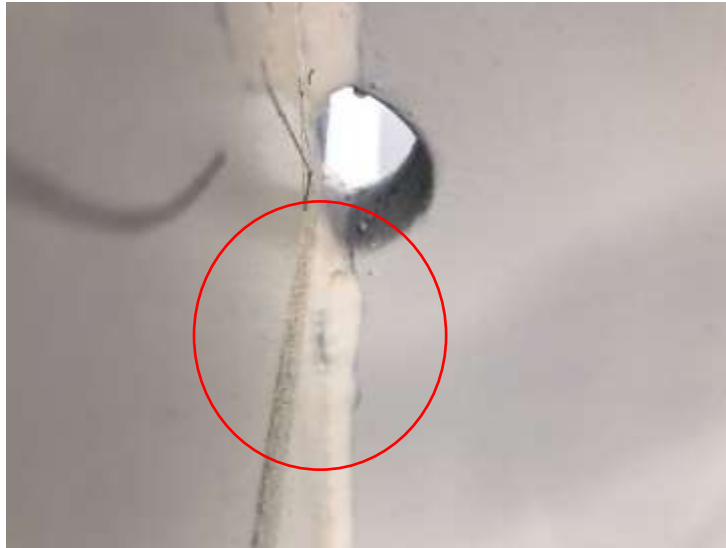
Exceso de soldadura [Fuente: Propia 2023]
